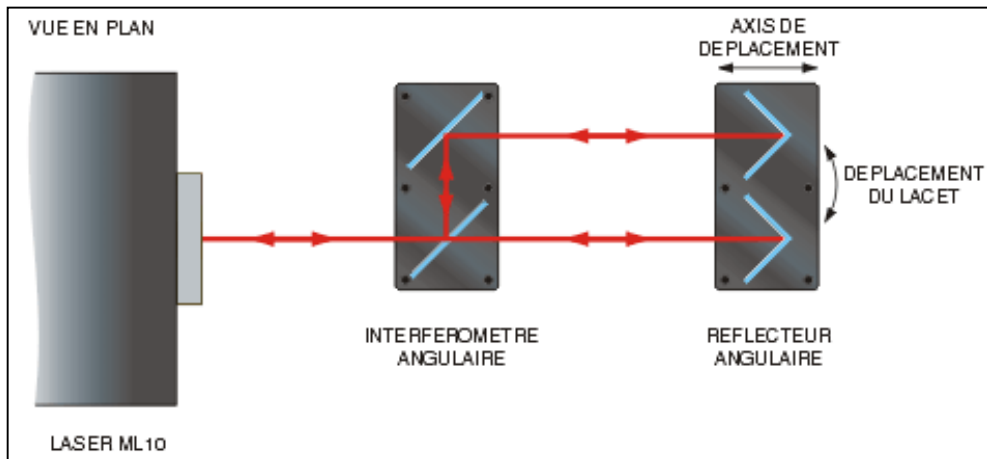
Mesure d'erreur de lacet - axe horizontal.
